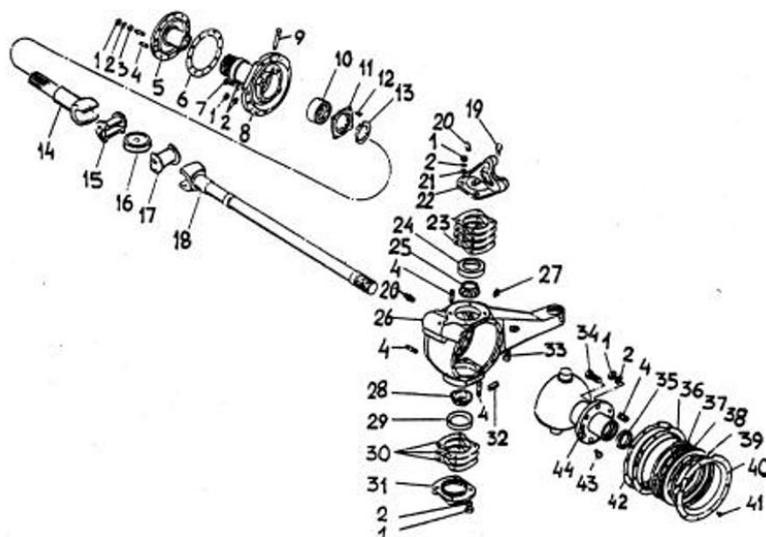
Поворотный кулак автомобиля КамАЗ 6х6:
